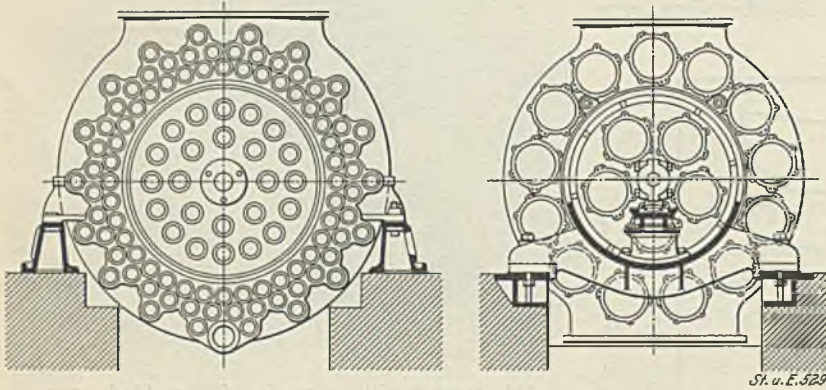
Gewöhnliches Ventilgehäuse. Borsig - Ventilgehäuse.
